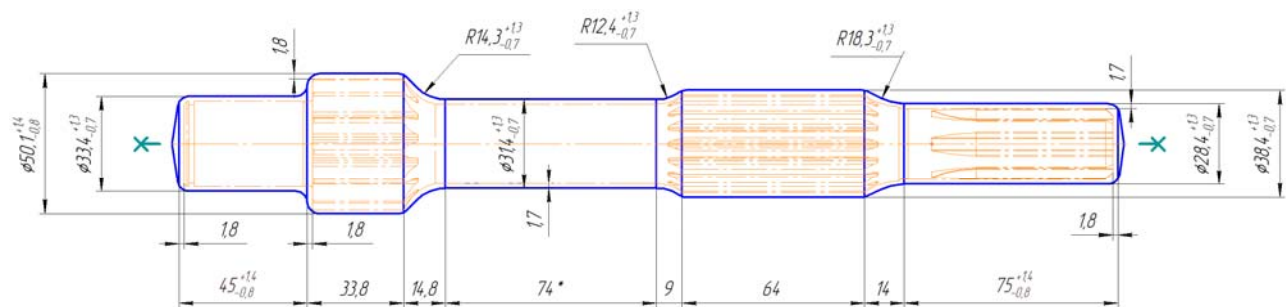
Ескіз заготовки – штамповки на кривошипному гарячо-штампувальному пресі
